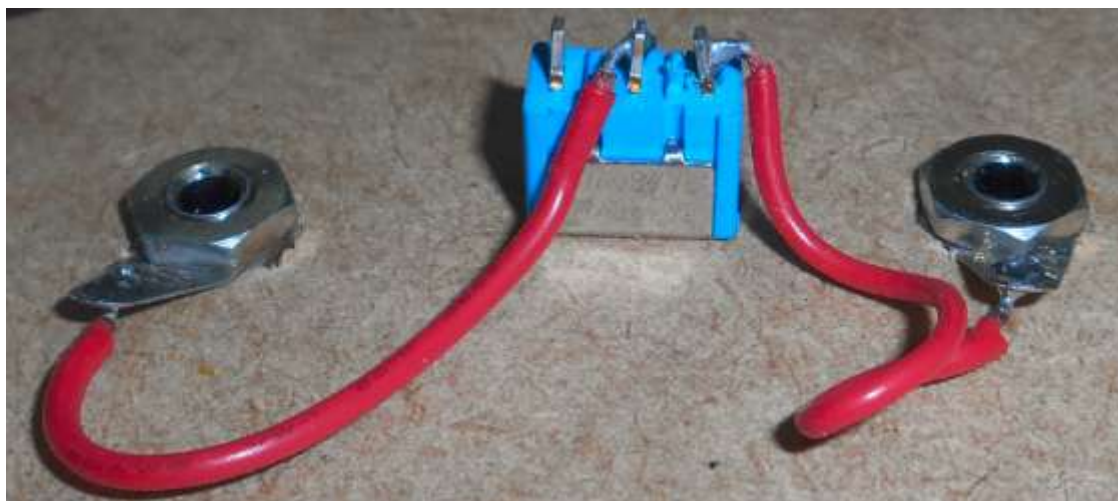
detalhes da ligação do interruptor (visto por baixo do painel). Fonte: O autor.
